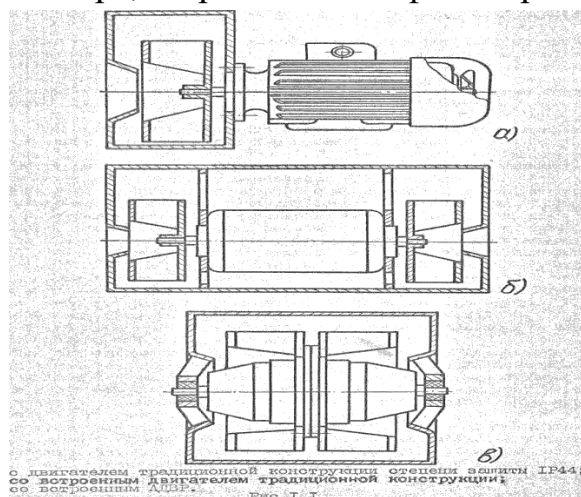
Схема вентиляторної установки з вбудованим АДЗР
